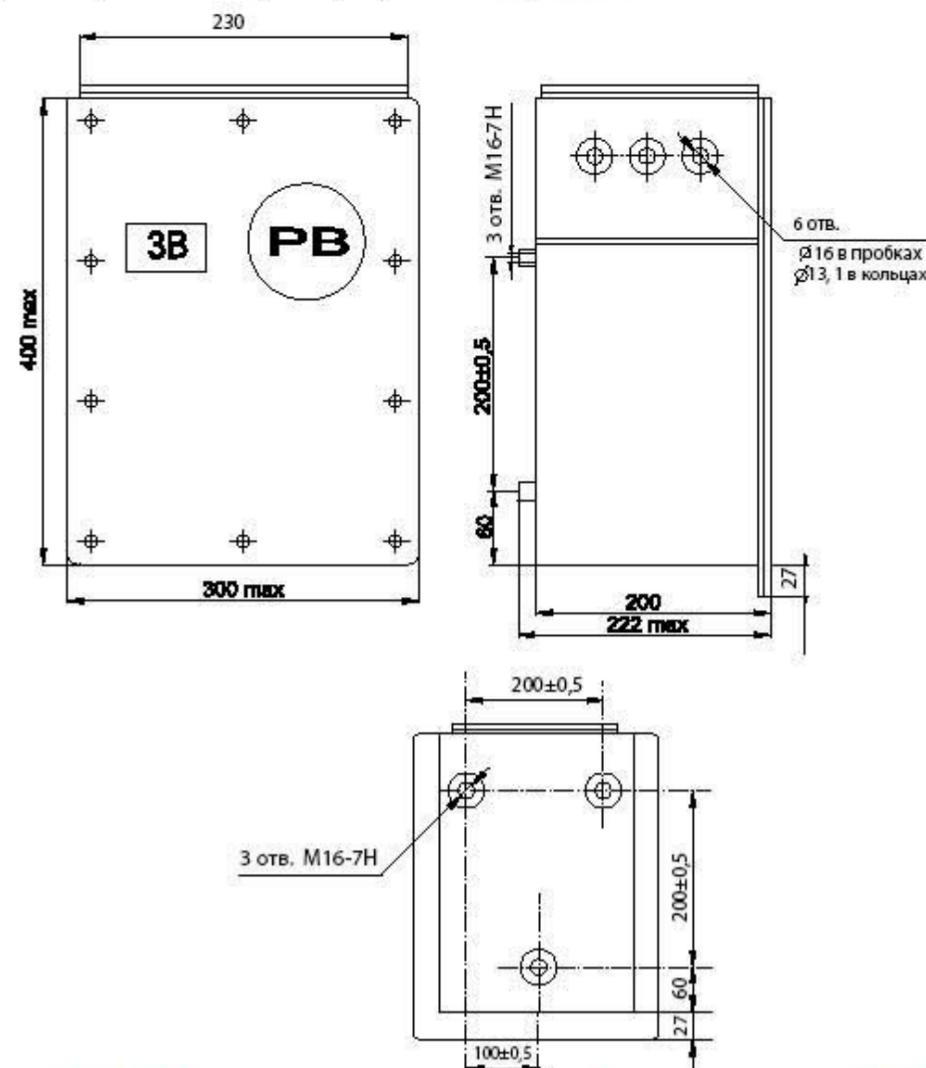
Габаритные и установочные размеры стабилизатора на напряжения СНВ-2М
